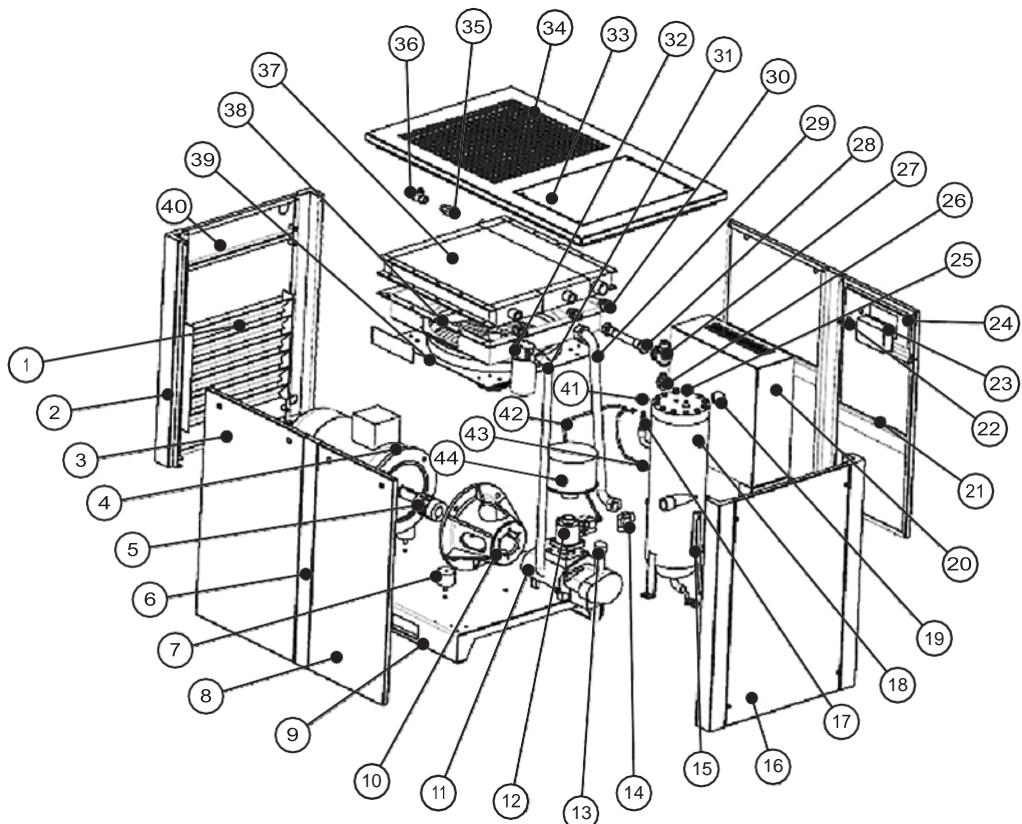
Деталировка на винтовой компрессор с прямым приводом серии IC 75-175 D
